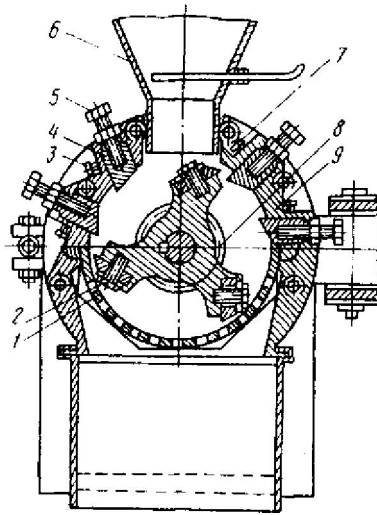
Схема роторного ножового подрібнювача ИПР-150
